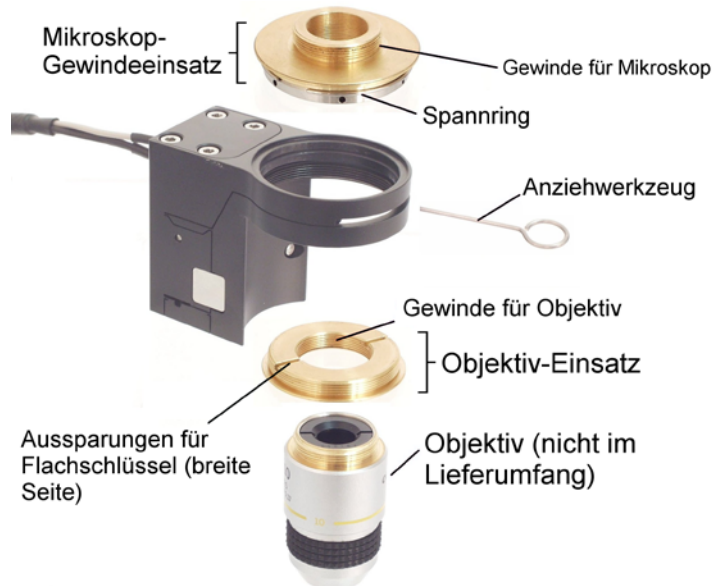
P-721.xxQ: PIFOC® Positionierer mit QuickLock-Adapter und Mikroskop-Objektiv. Ein QuickLock-Adapter besteht aus einem Mikroskop-Gewindeeinsatz und einem Objektiv-Einsatz. Das Anziehwerkzeug ist im Lieferumfang enthalten.
